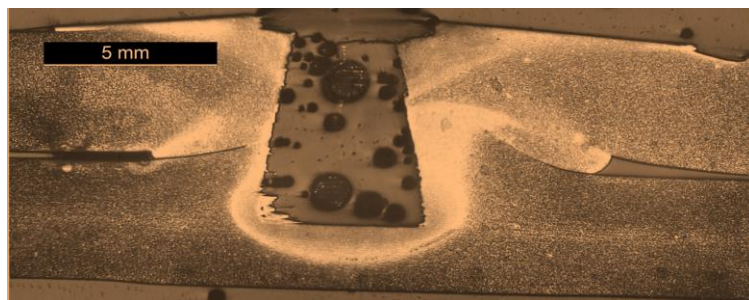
Macrografia do perfil de soldadura do provete S500B-1, realizado com recurso à ferramenta B com pino de 5 mm e velocidade de rotação de 500 rpm
